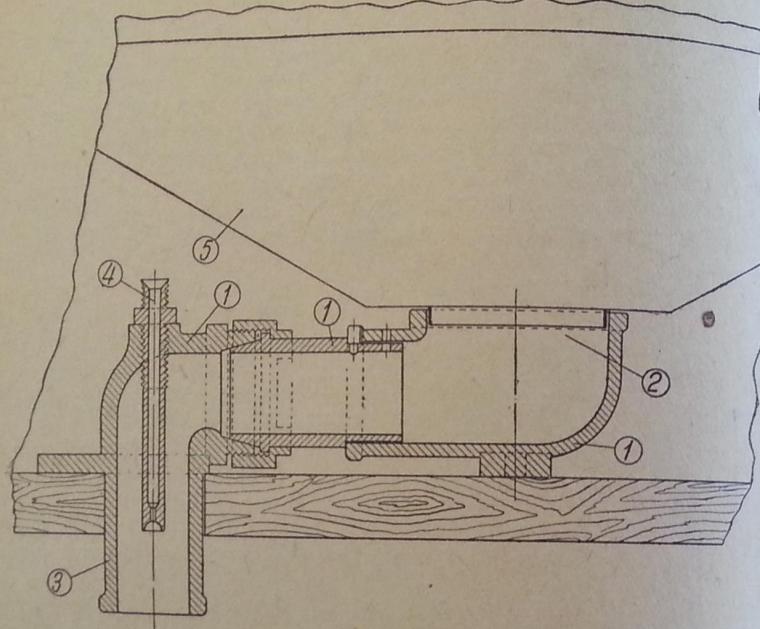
Воздушная песочница Плашинского: 1 — корпус, 2 — отверстие, 3 — патрубок, 4 — сопло, 5 — песочный ящик.
